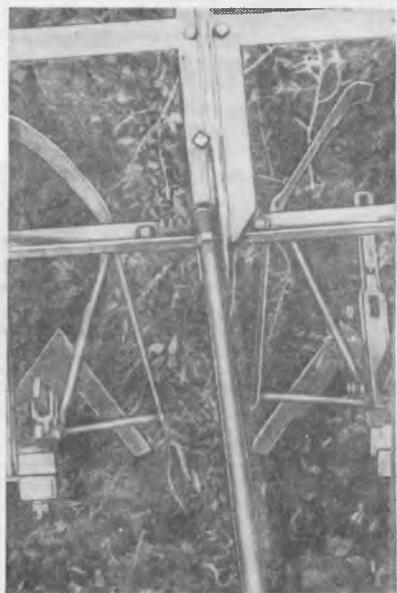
Приспособление к культиватору КЛТ-4,5Б (вид сверху).
